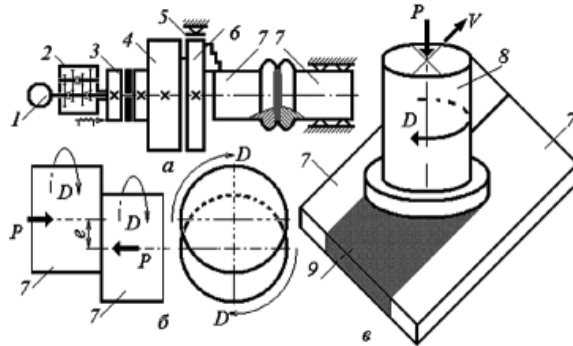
Схеми зварювання тертям: а – інерційне; б – орбітальне; в – з перемішуванням; 1 – електромотор; 2 – коробка швидкостей; 3 – електромагнітна муфта; 4 – маховик; 5 – гальмо; 6 – патрон; 7 – зварювані заготовки; 8 – індентор; 9 – зварний шов;  $D, V$  – обертальний і поступальний рух;  $P$  – тиск проковки
